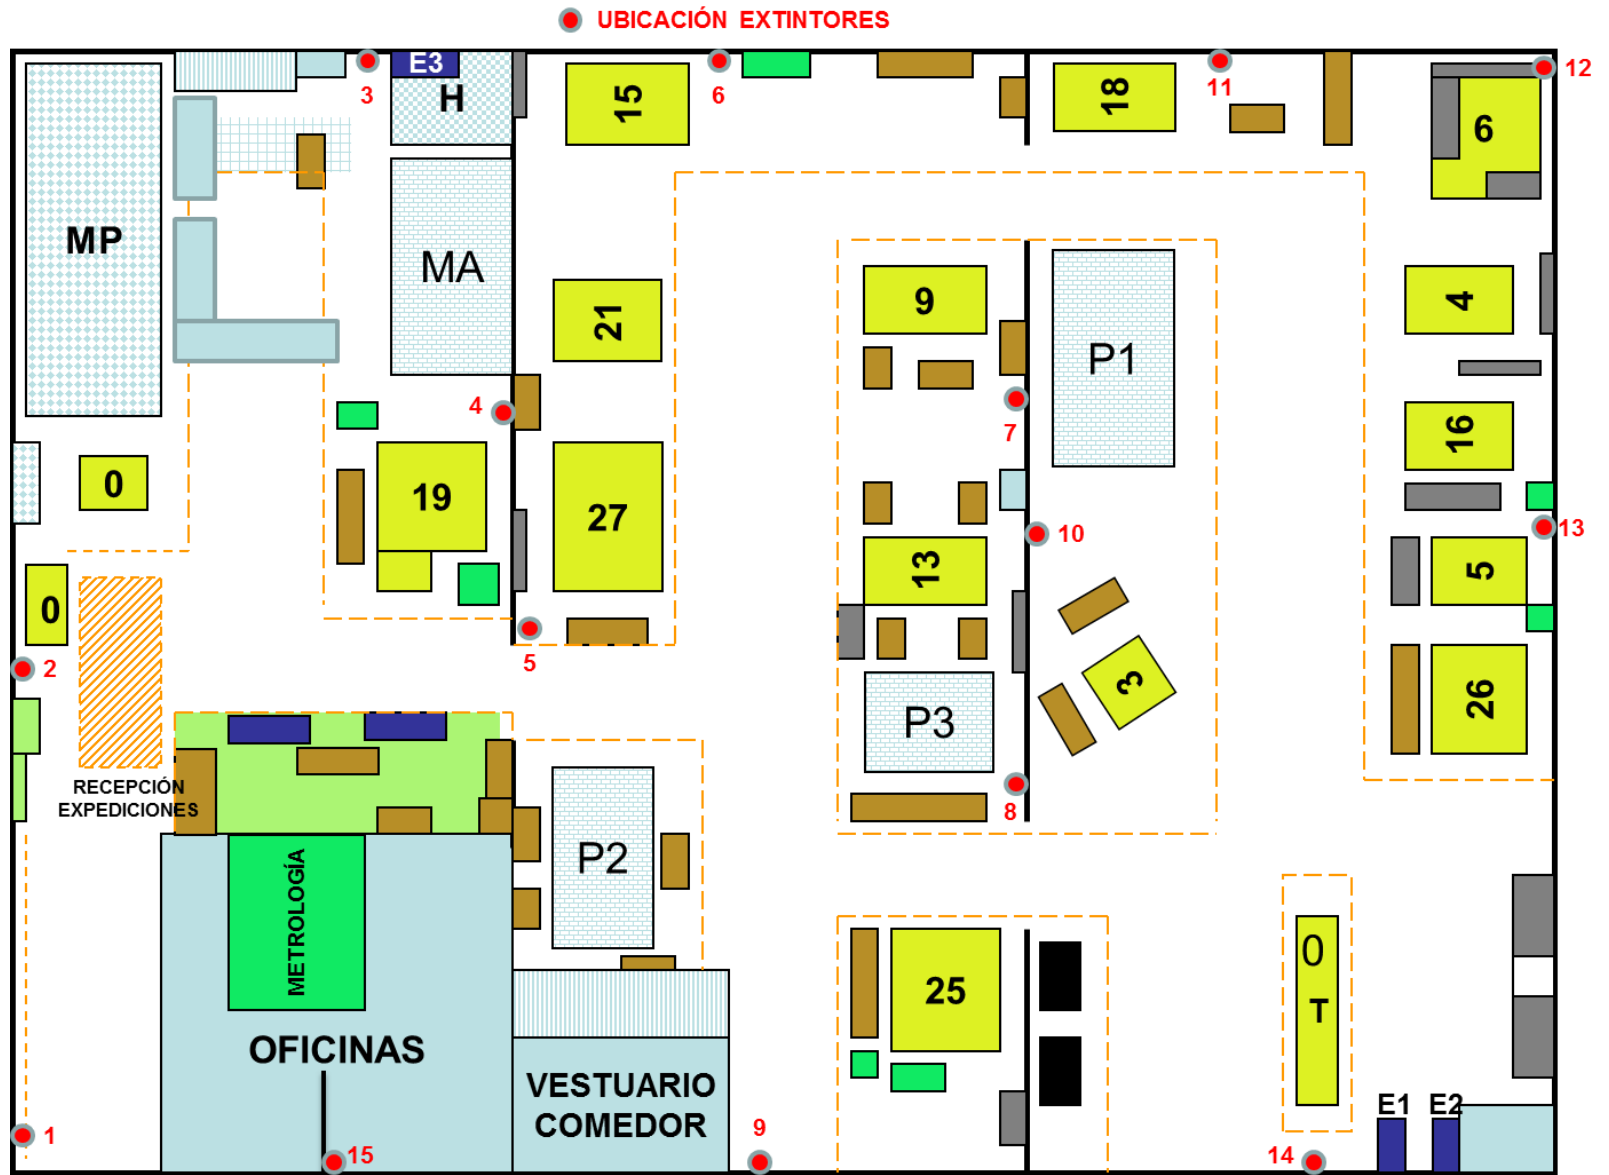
Distribución de planta actual (Facilitado por la empresa)
